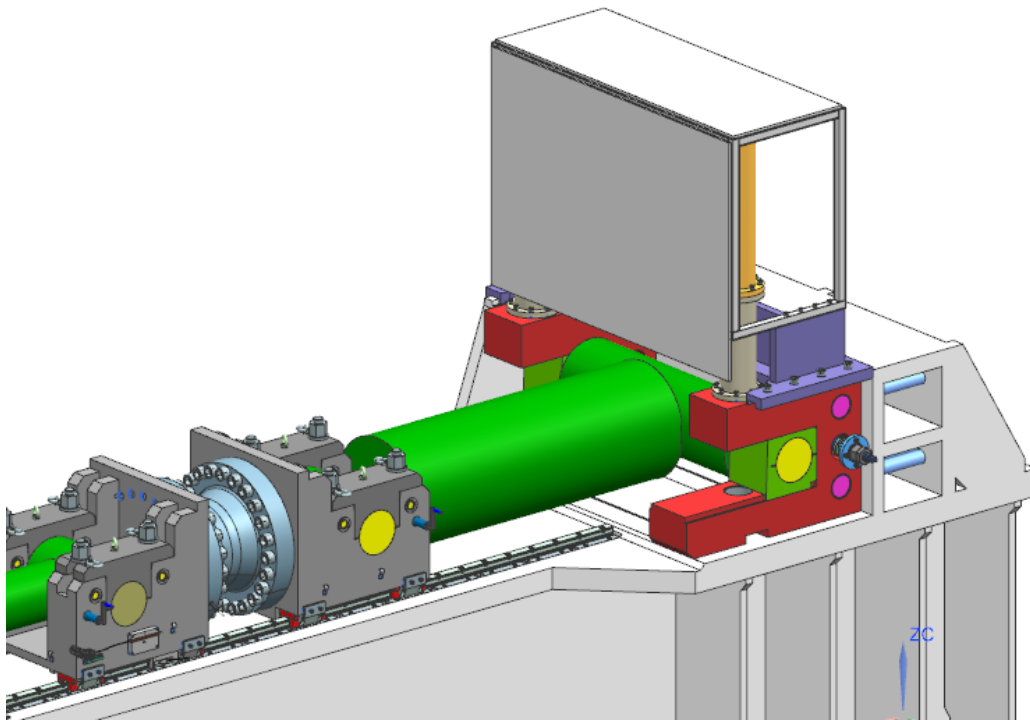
Upevnění testovaného HM – dopravení hydromotoru
